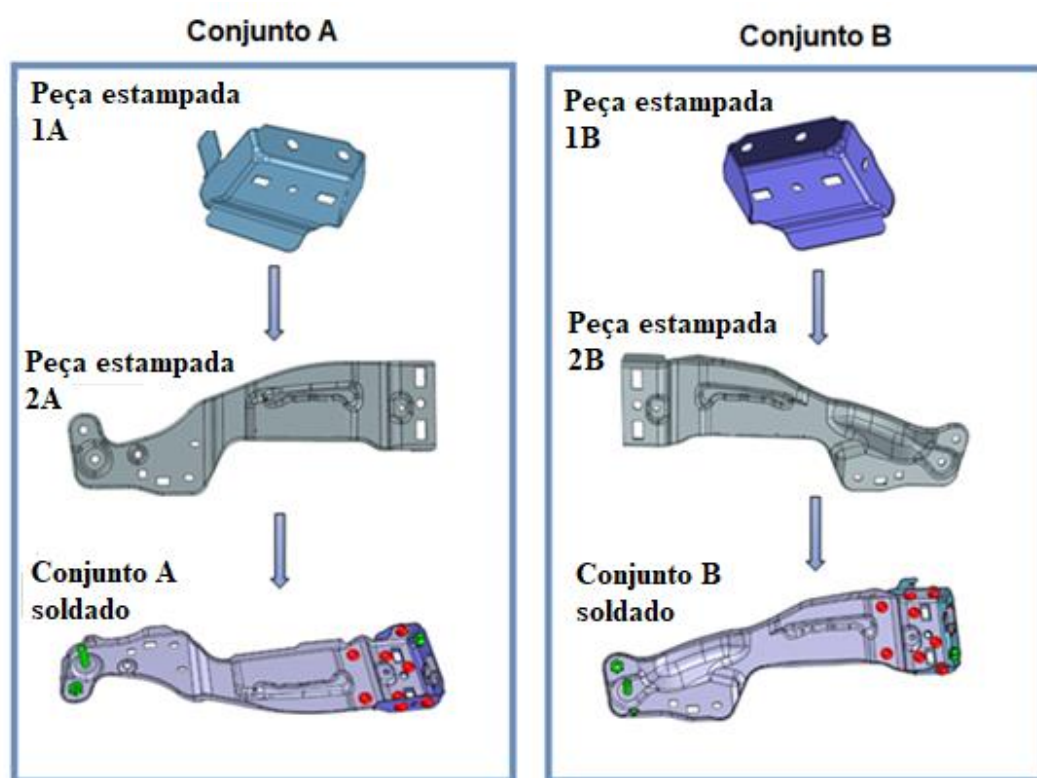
Conjuntos soldados A e B (Produtos/Co-Produtos)
